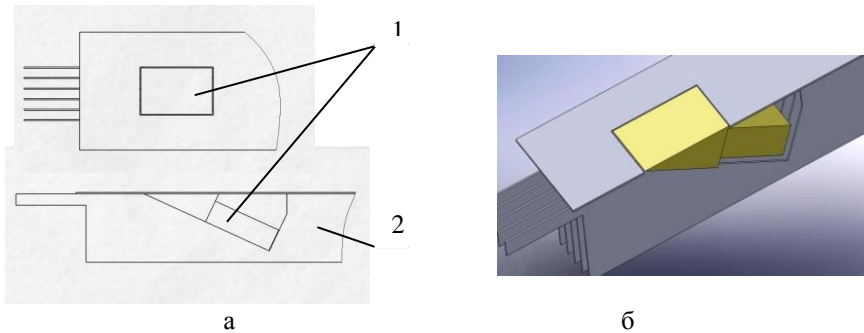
Пример схемы (а) и общий вид (б) приспособления для термической обработки зуба экскаватора (1 – зуб экскаватора; 2 – приспособление для крепления)
